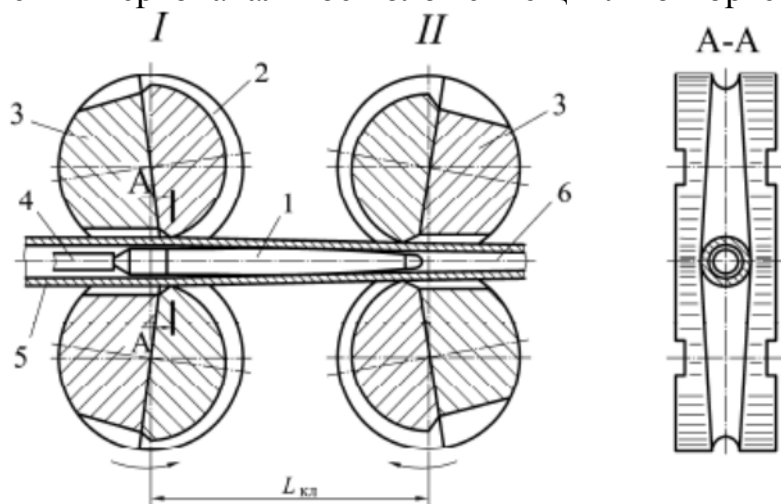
Схема прокатки труб на стане ХПТ: 1 – оправка; 2 – калибр; 3 – валок; 4 – стержень; 5 – заготовка; 6 – труба
